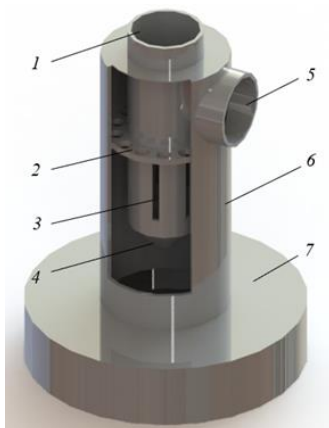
Сепарационный модуль: 1 – патрубков для подачи газа; 2 – решетка с трубами, расположенными коаксиально; 3 – отверстия прямоугольной формы; 4 – отверстие для сброса материала; 5 – патрубков для выхода газа; 6 – корпус; 7 – сборный бункер
